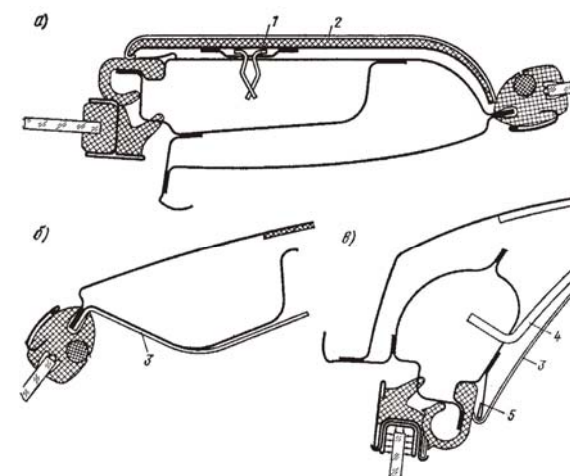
Крепление обивки задней части боковины и обивки потолка:
